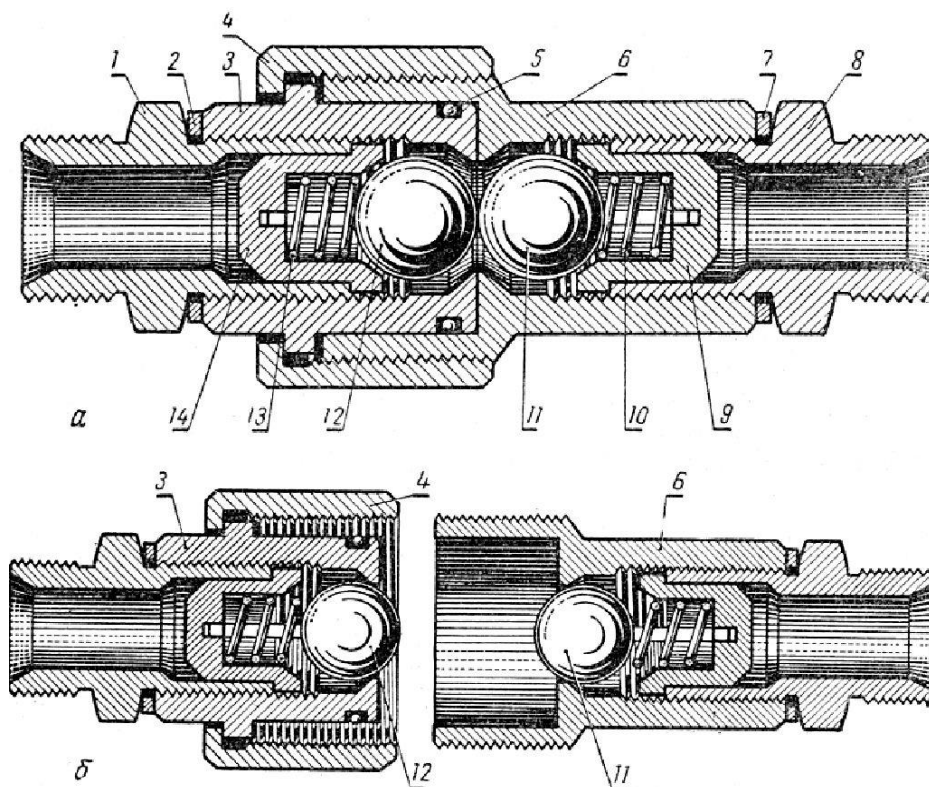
Соединительная муфта (запорное устройство): *а* - маслопроводы соединены; *б* - маслопроводы разъединены; 1, 8 - проходные штуцеры; 2, 7 - уплотнительные шайбы; 3 - левый корпус клапана; 4 - накидная гайка; 5 - резиновое уплотнительное кольцо; 6 - правый корпус клапана; 9, 14 - крестовины; 10, 13 - пружины клапанов; 11, 12 - шарики
